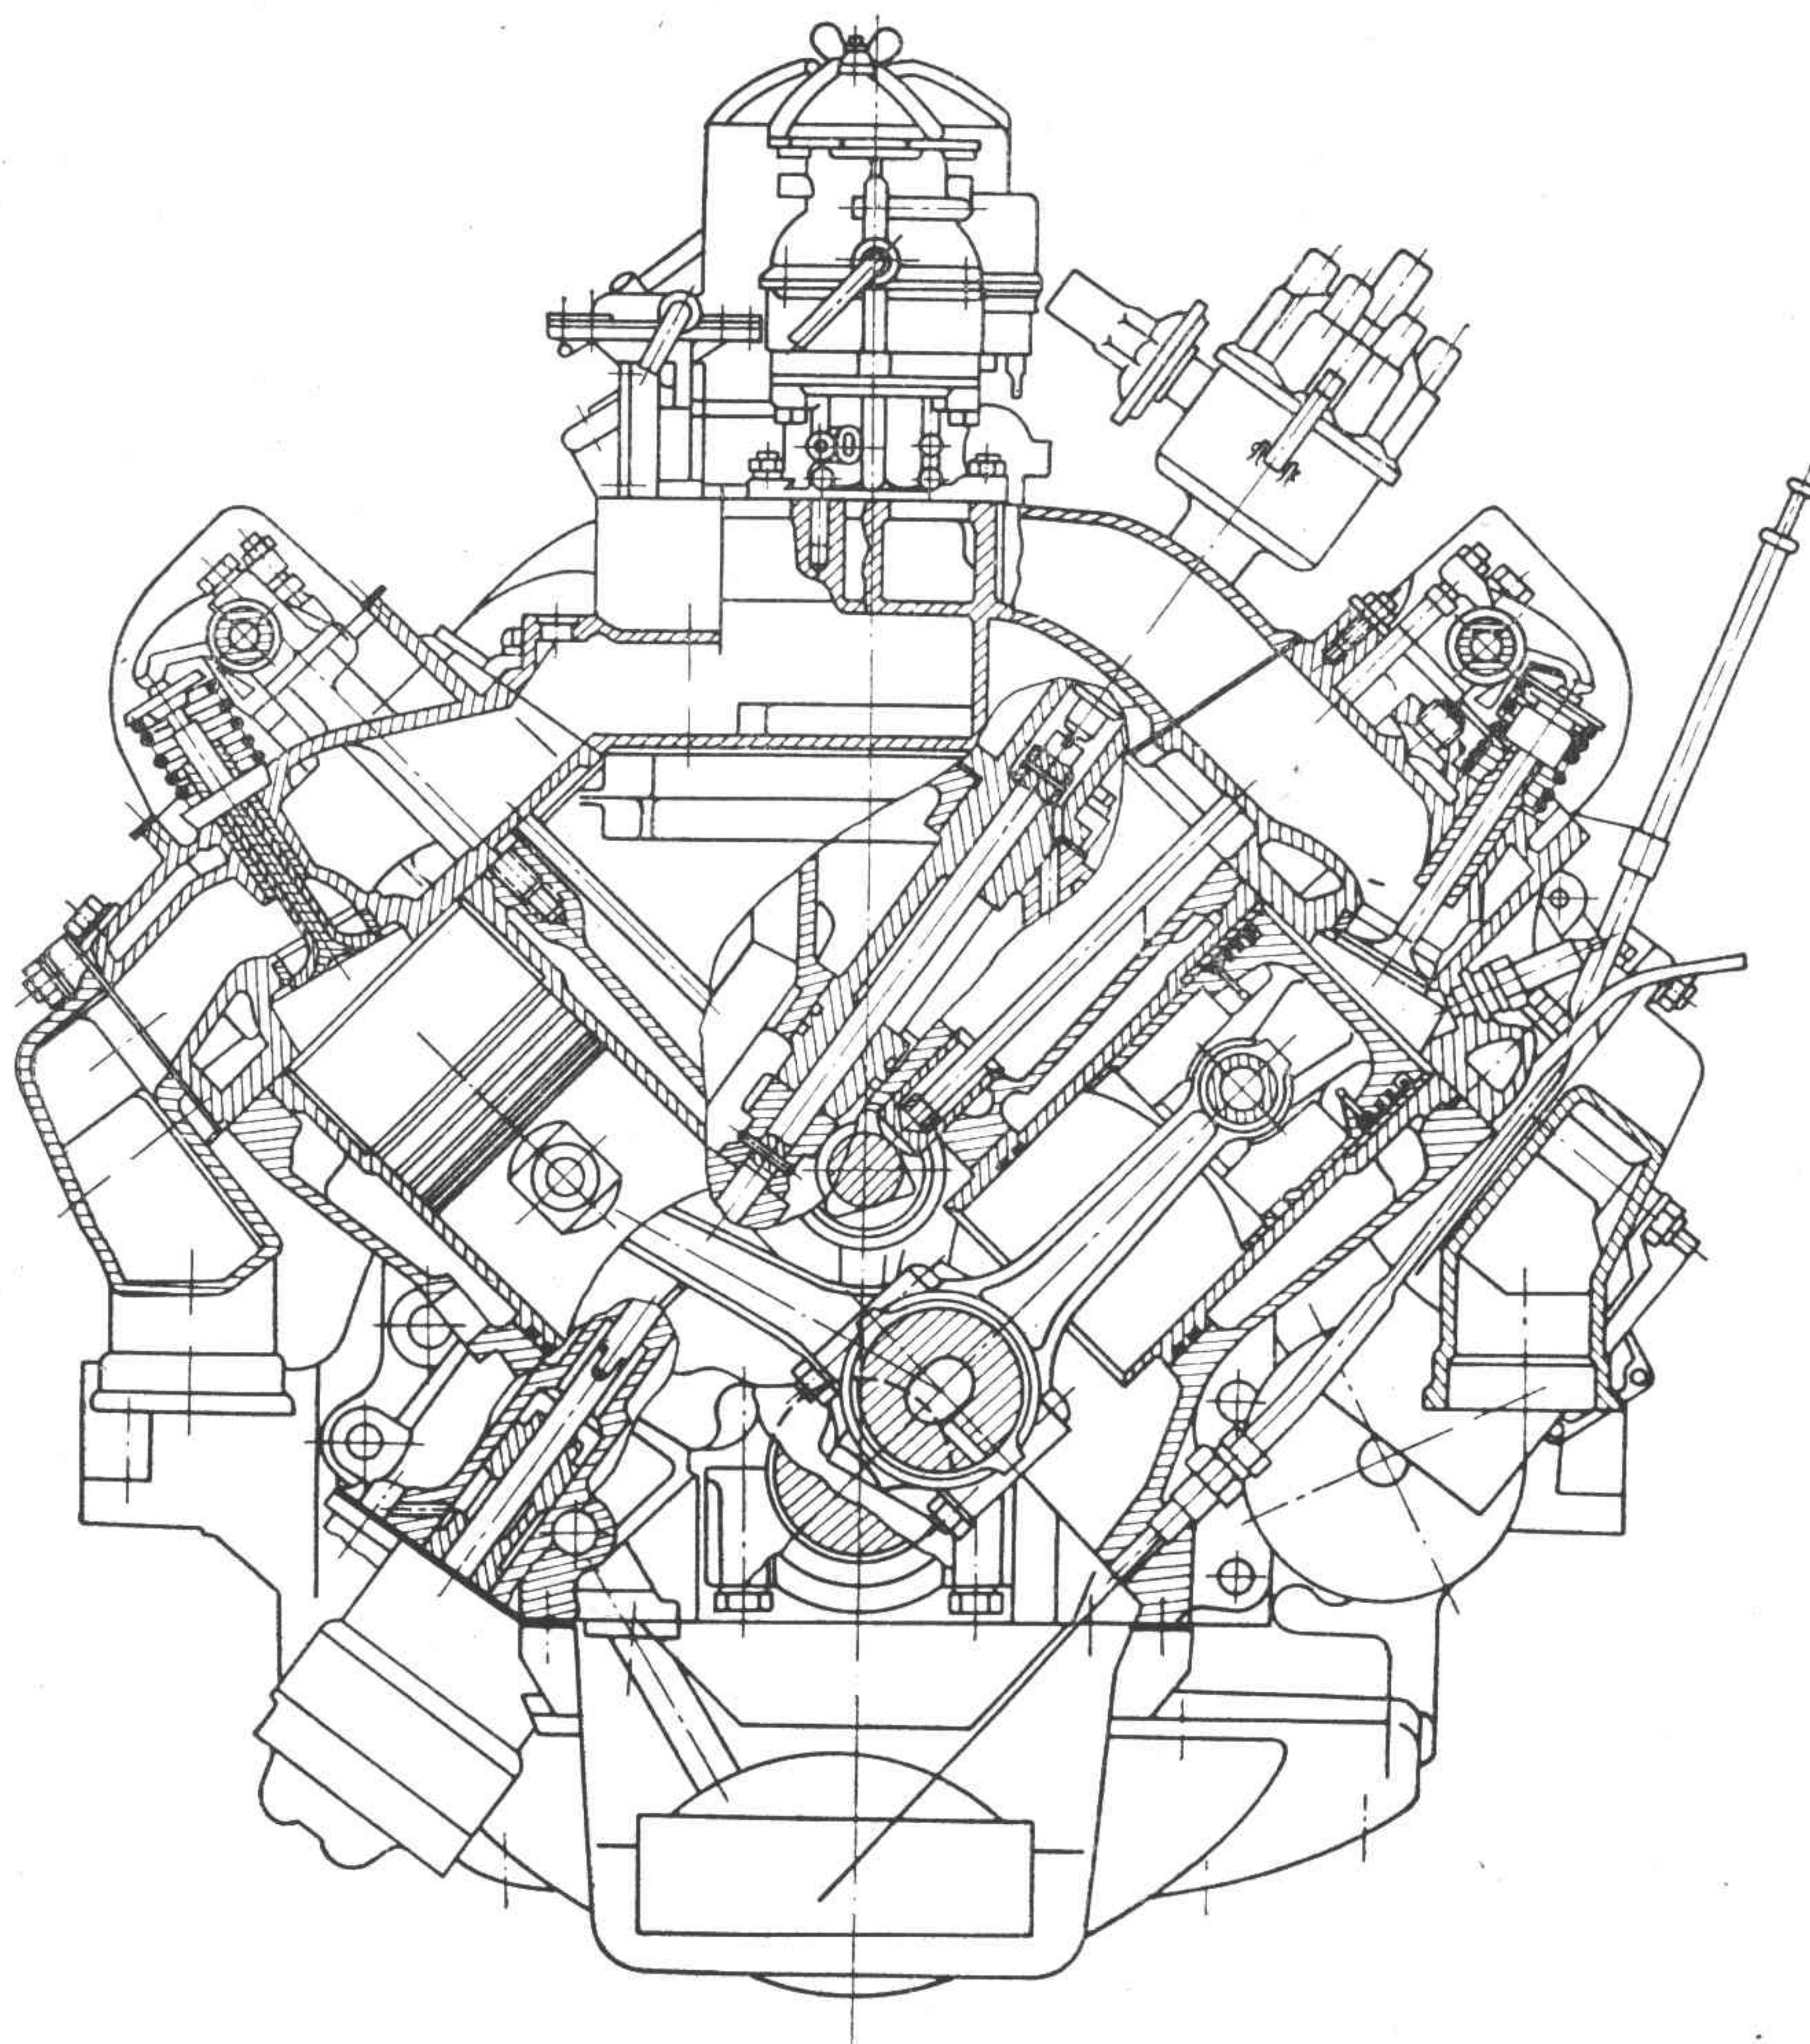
Поперечный разрез двигателя ЗИЛ-130, ЗИЛ-375
